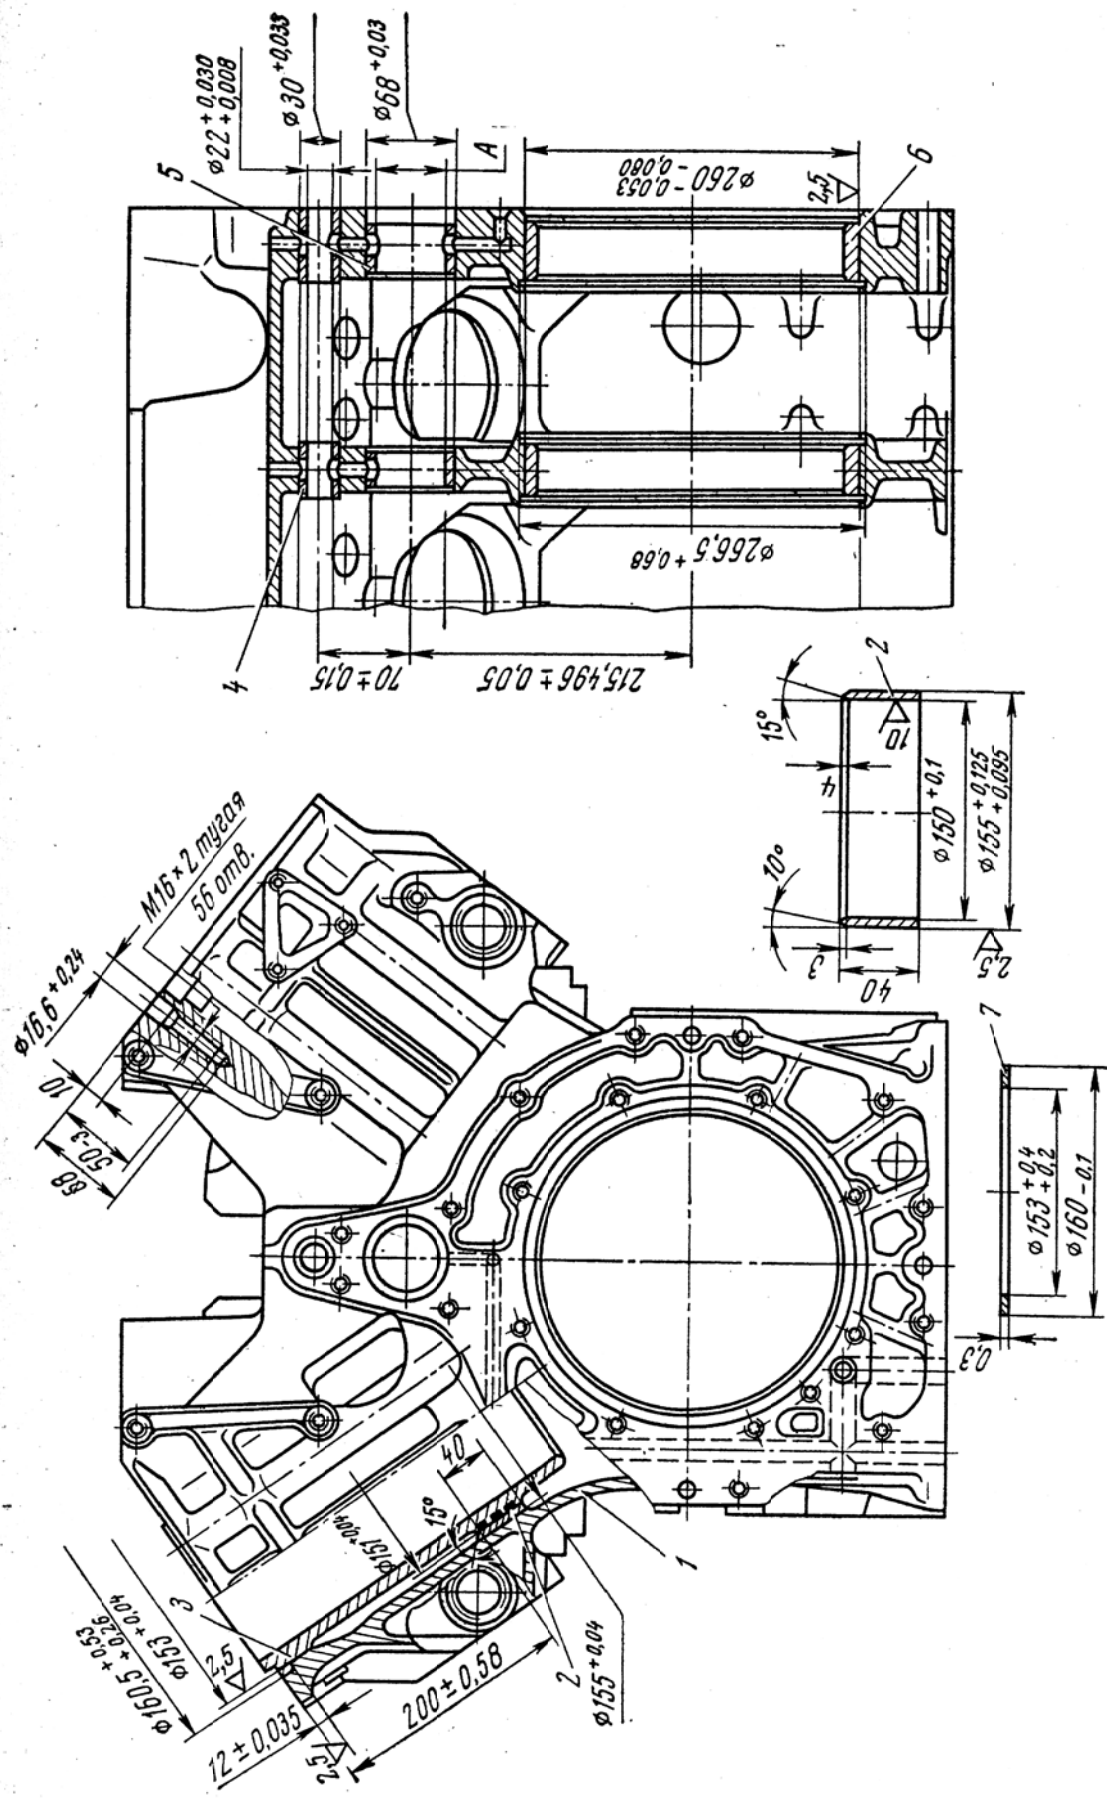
Блок цилиндров двигателя ЯМЗ-240НБ
